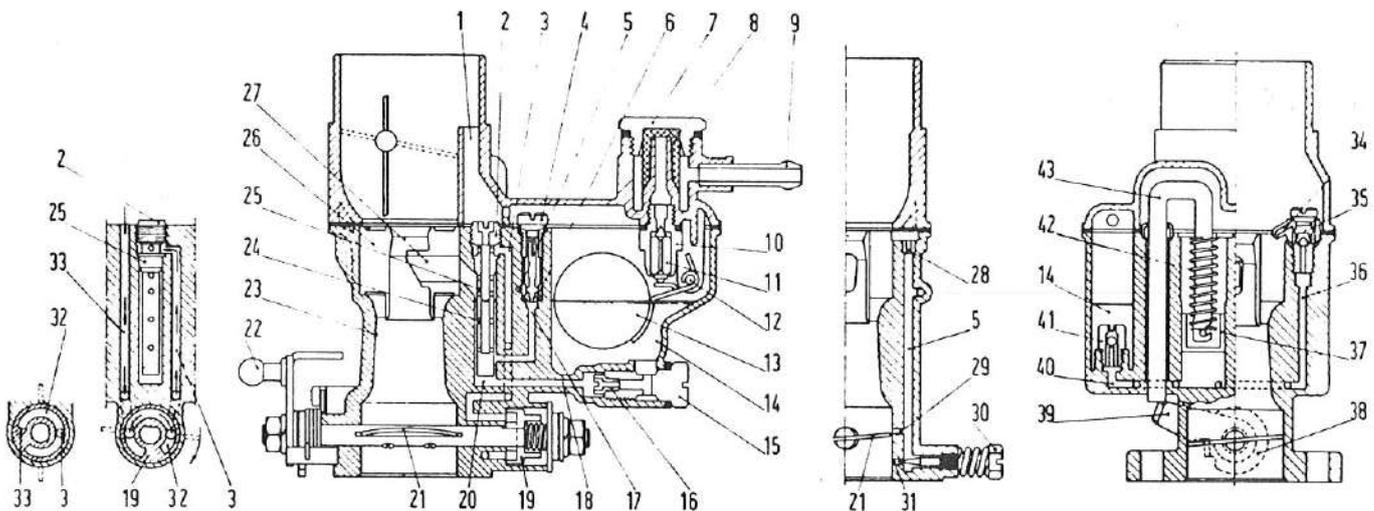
Secciones del carburador Bressel tipo 28 ICP 6.
